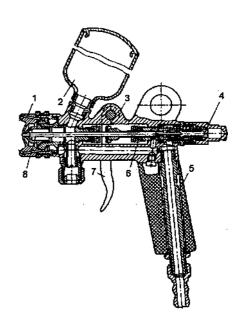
Пневматический пневмораспылитель: 1 — распылительная головка; 2 бачок для краски; 3 — корпус распылителя; 4 — запорный винт; 5 — ручка; 6 прокладка; 7 — спусковой крючок; 8 — запорная игла
